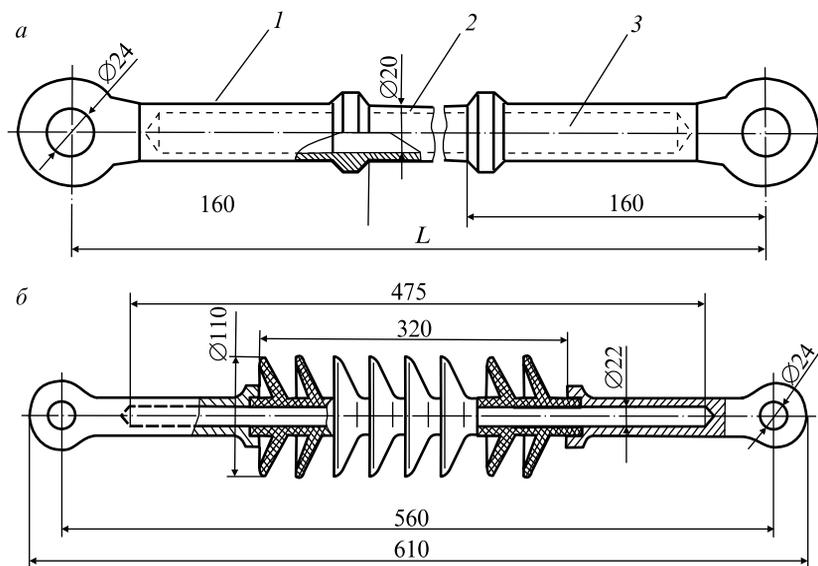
Полимерные натяжные изоляторы: а — НСФТ120/1,2 с фторопластовой защитной трубой; б — НСКр120/0,95 с ребристым защитным чехлом из кремнийорганической резины; 1 — оконцеватель; 2 — защитная трубка; 3 — полимерный стержень
